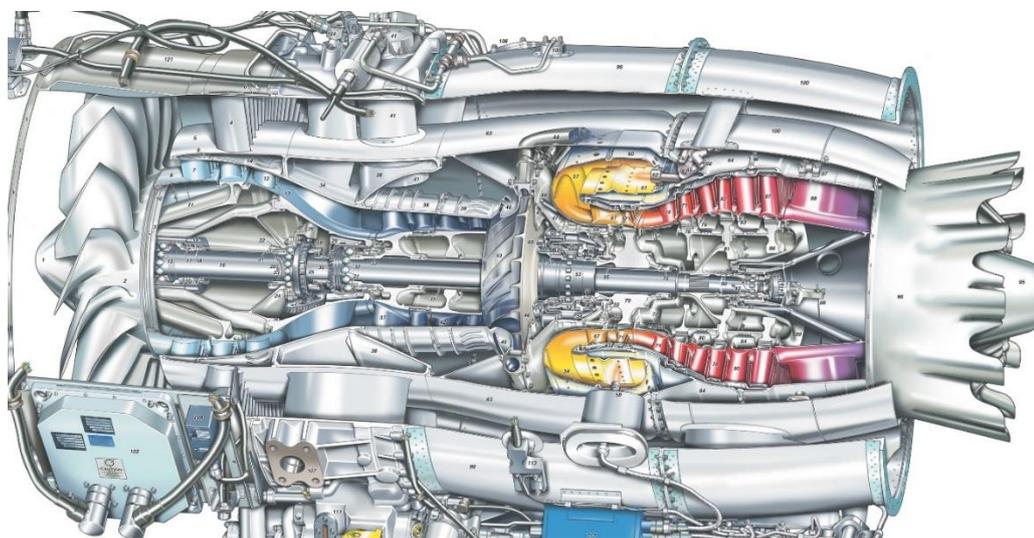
ГТД PW 545 с осецентробежным компрессором [8]
